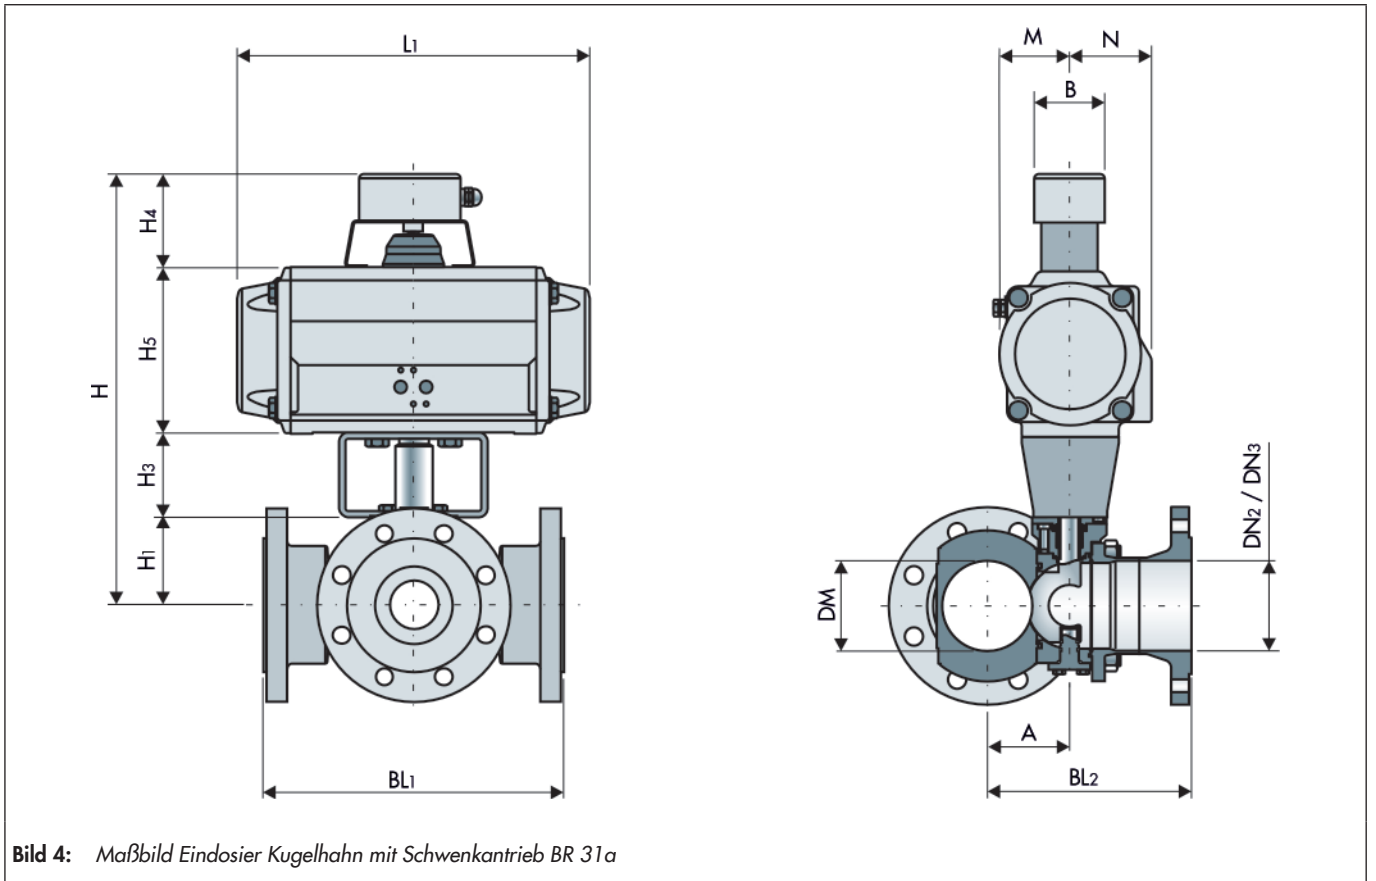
Maßbild Eindsier Kugelhahn mit Schwenkantrieb BR 31a
